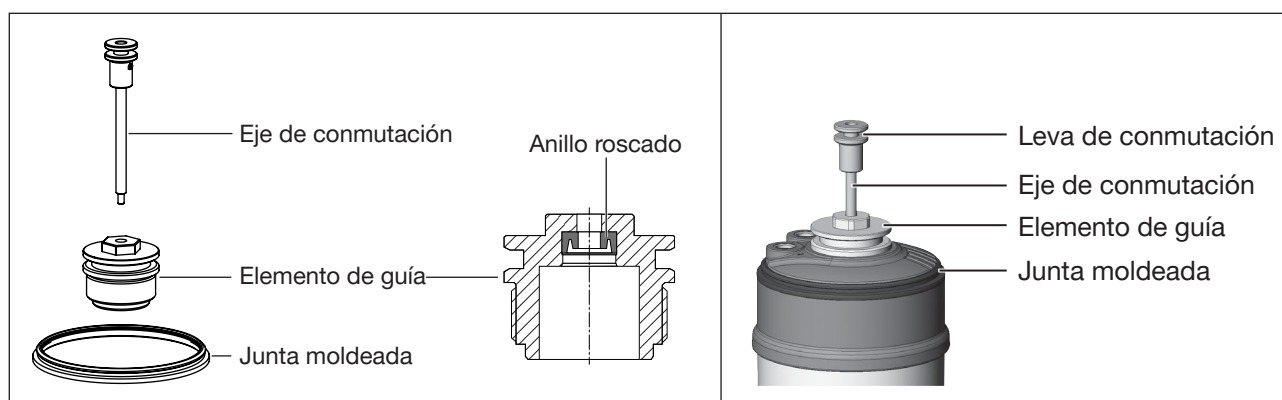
Kit de montaje «transductor de desplazamiento remoto» Actuador con kit de montaje instalado
